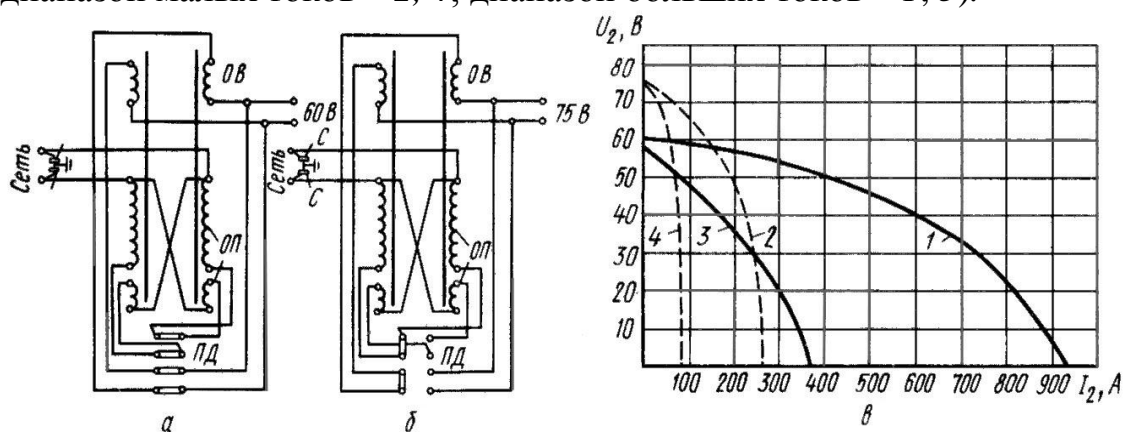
Сварочный трансформатор типа ТД
